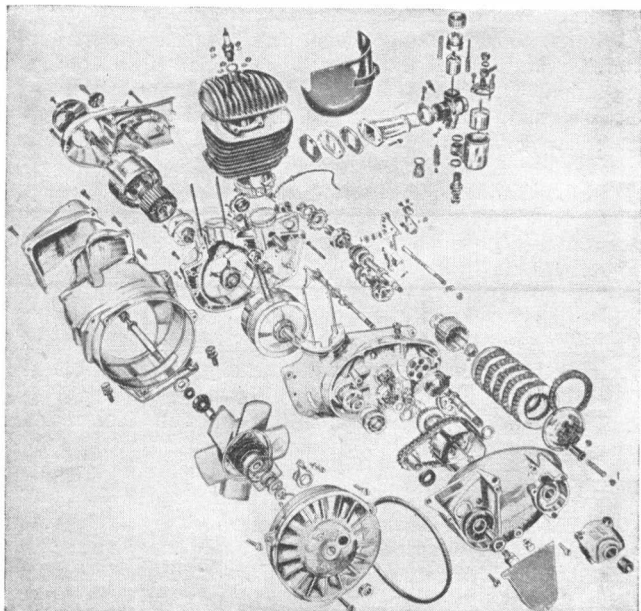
Explosivzeichnung des Motorrollermotors RM 150
